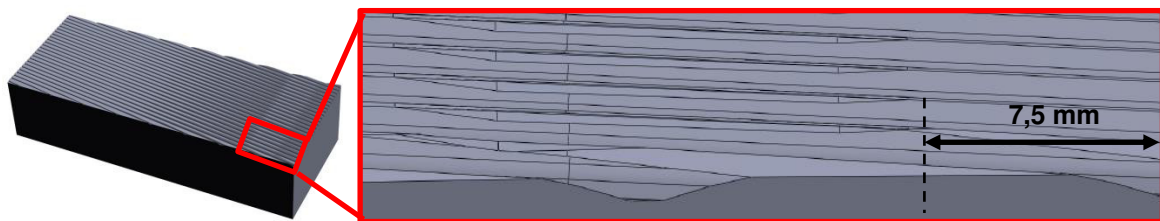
3D-CAD-Modell einer verschlissenen langen Walzbacke
